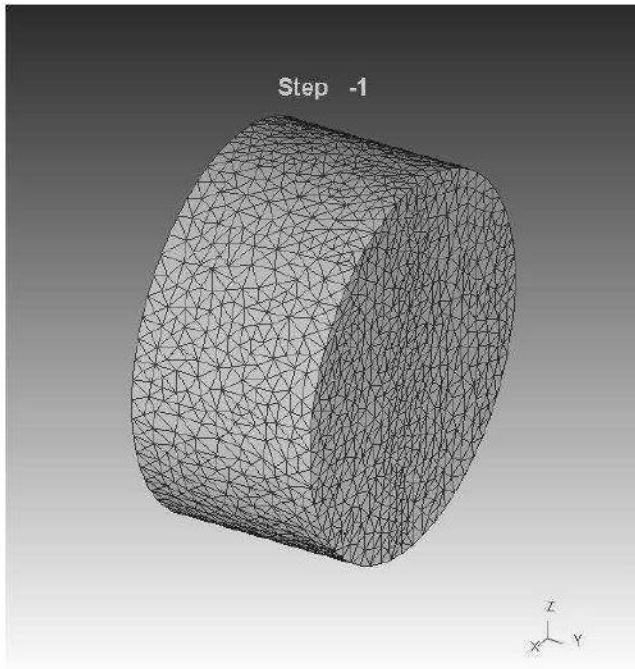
Розбиття заготовки ( $\varnothing = 60$  мм) на 20 000 кінцевих елементів
